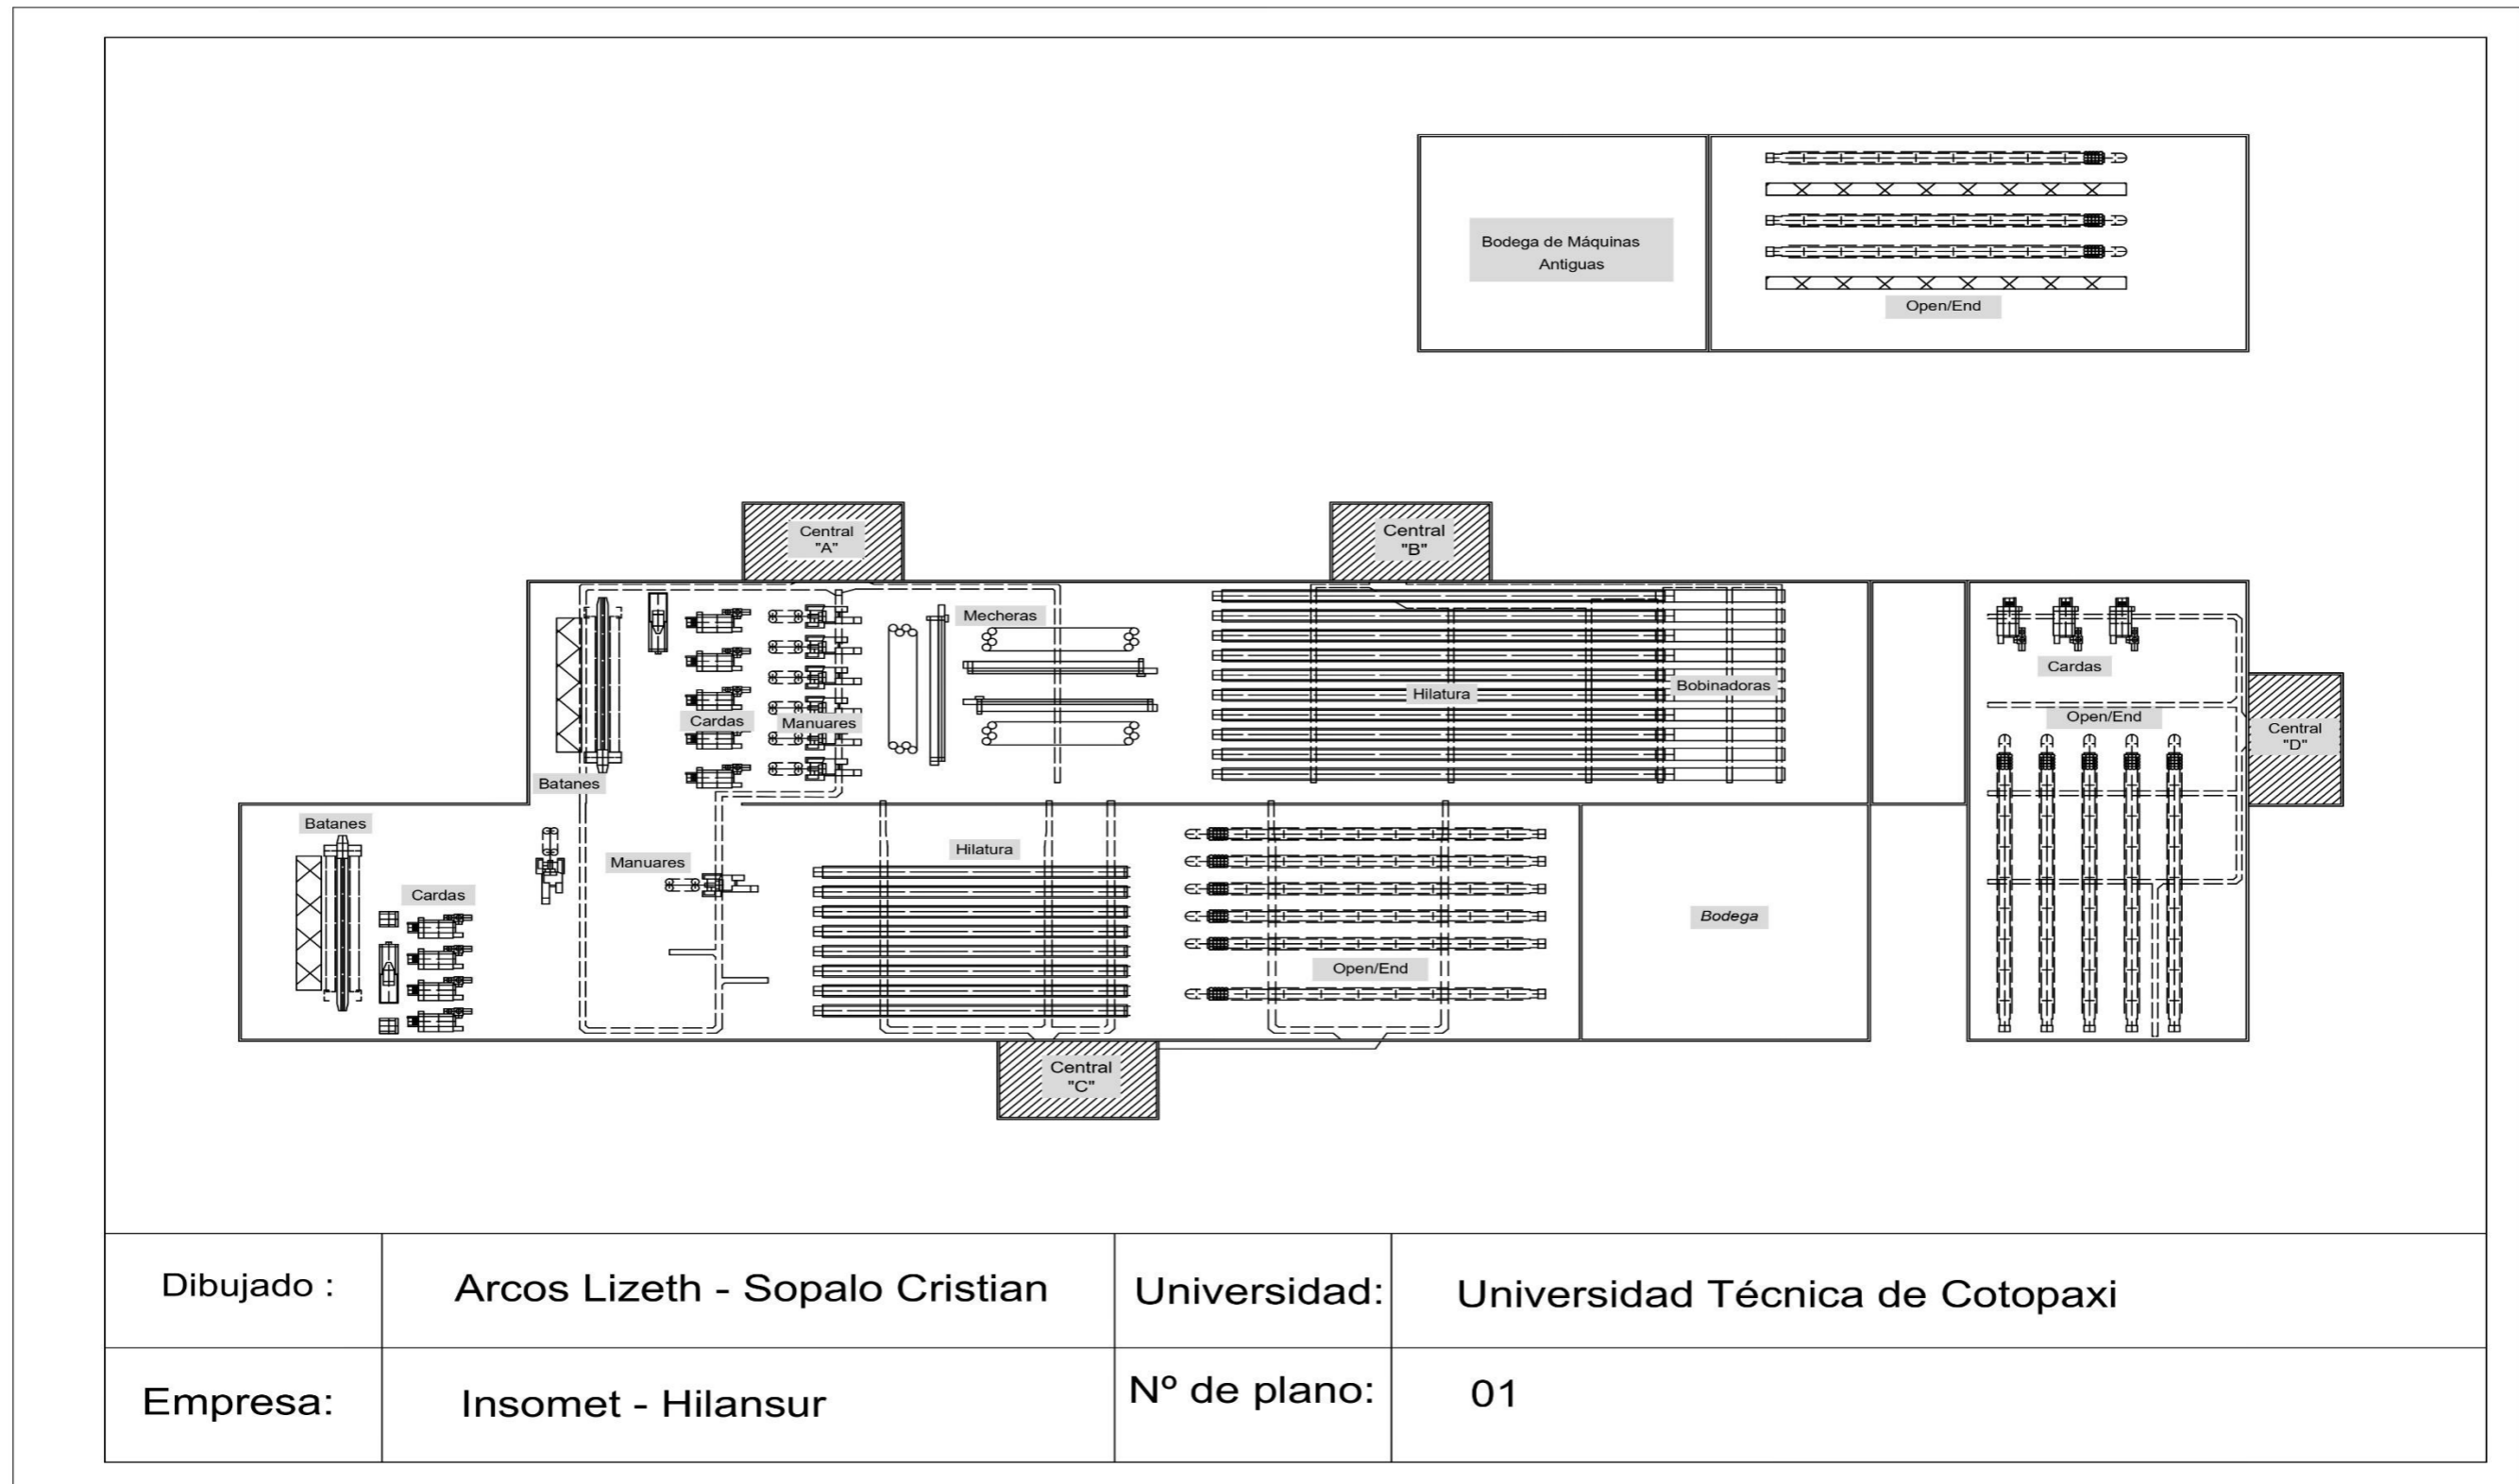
Layout de la empresa Insomet - Hilansur
